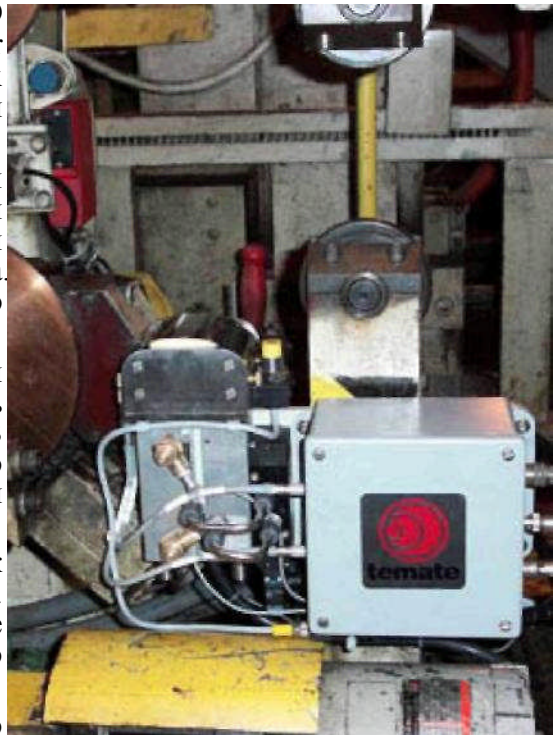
Каретка с датчиком и приводом в сварочном агрегате
